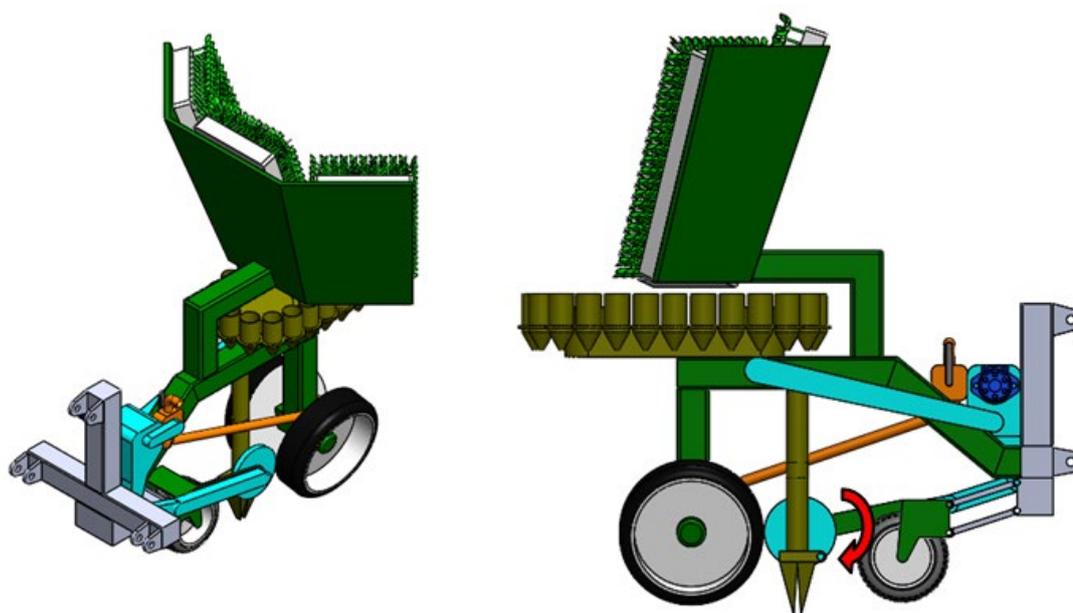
Concepção 4 da transplantadora de mudas de tabaco.
